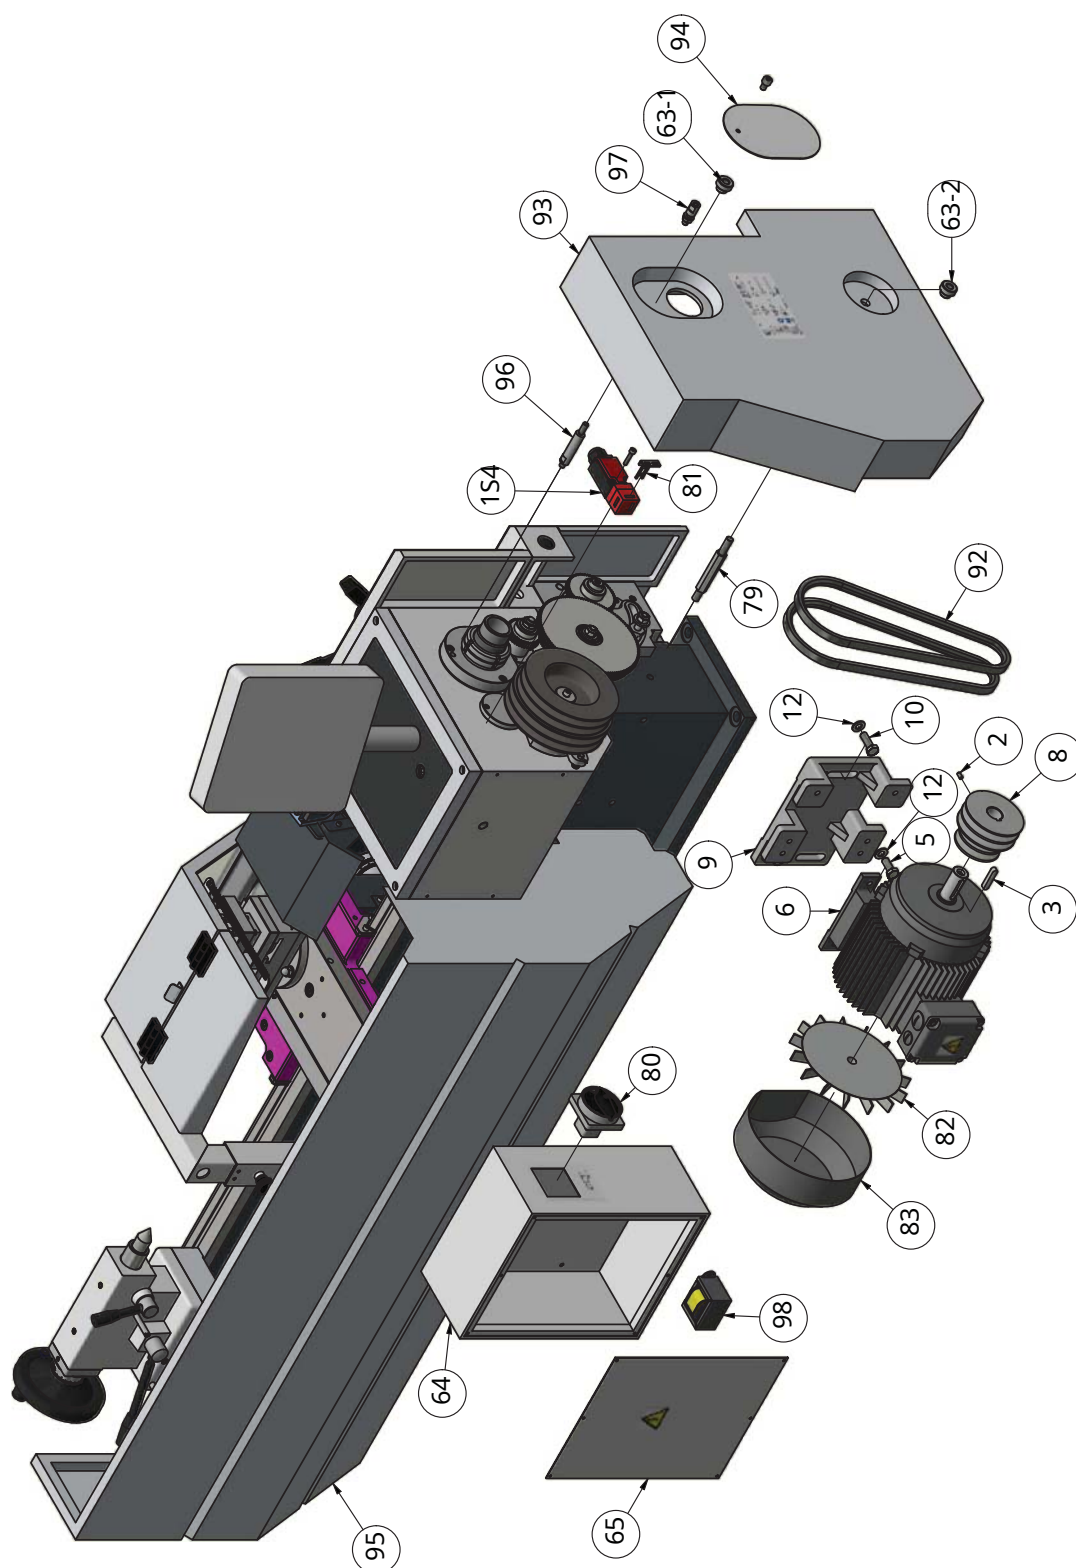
Maschinenbett 1-2 - Mesa de torno 1-2
